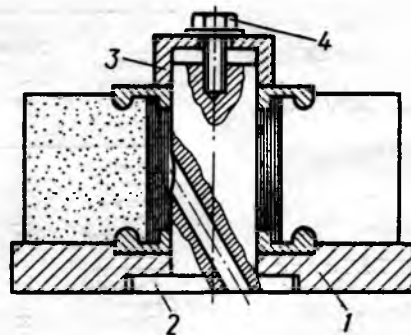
Оправка и схема сборки лепесткового шлифовального круга
